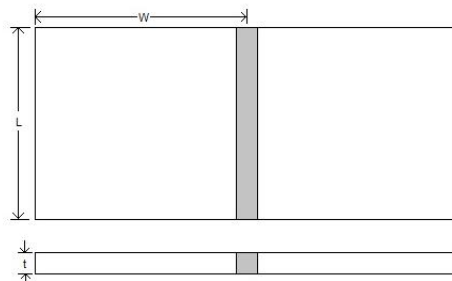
Dimensiones probeta para calificación de soldadura para posición 1G (chapa a tope)
